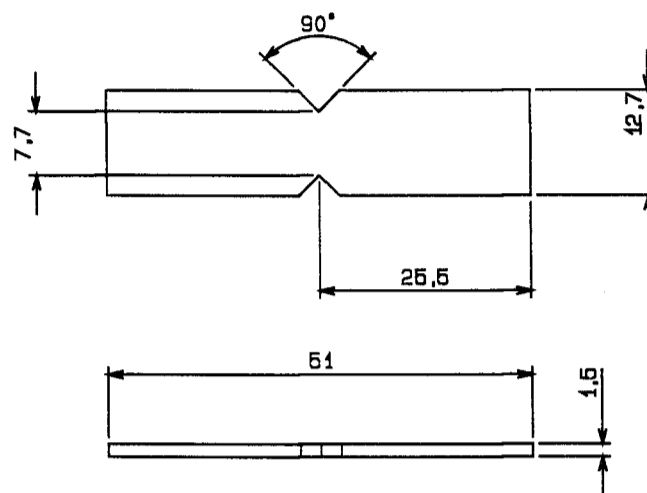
Geometria e dimensões do corpo-de-prova de cisalhamento longitudinal e transversal.
